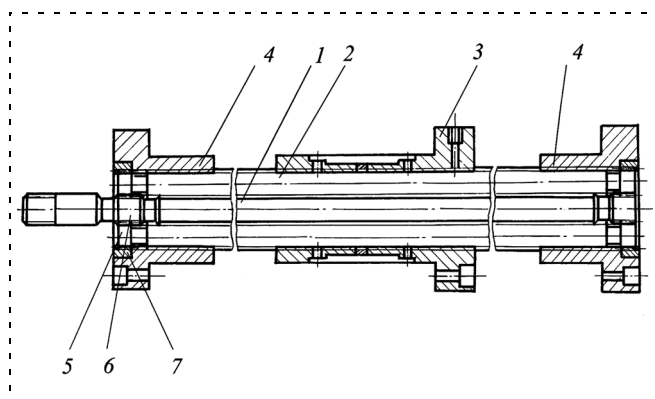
Планетарная передача с резьбовыми роликами и опорными гайками типа ЗК:
